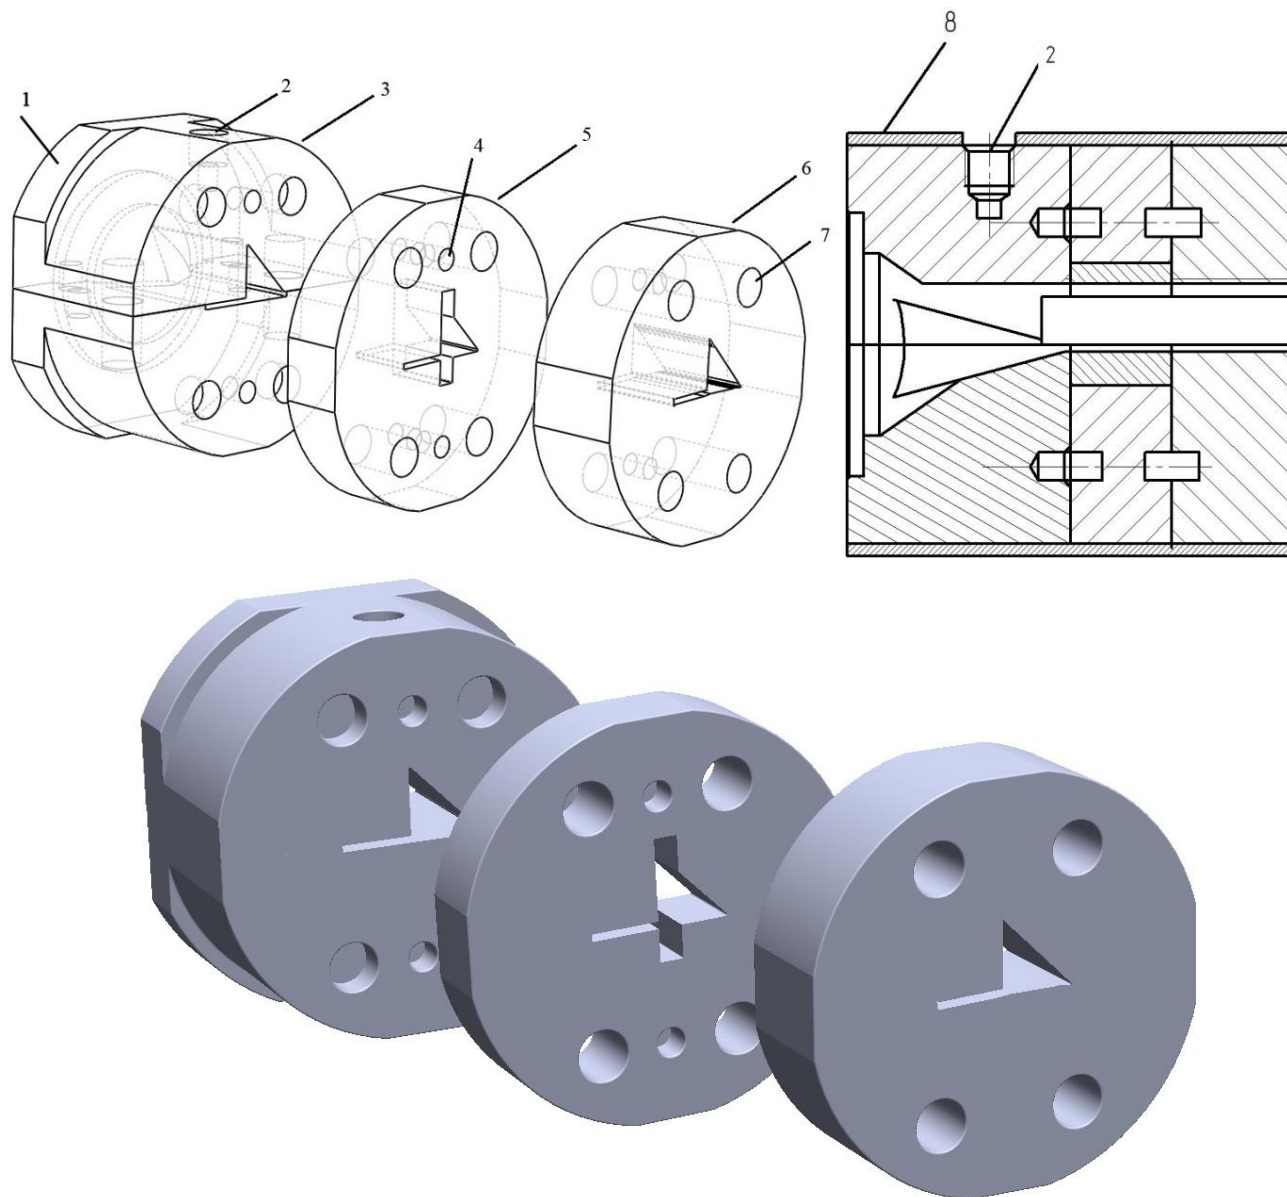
Змодельована головка для виробництва L-"подібного" однокамерного порожнього профілю: а) розібраний вид; б) вид в розрізі
